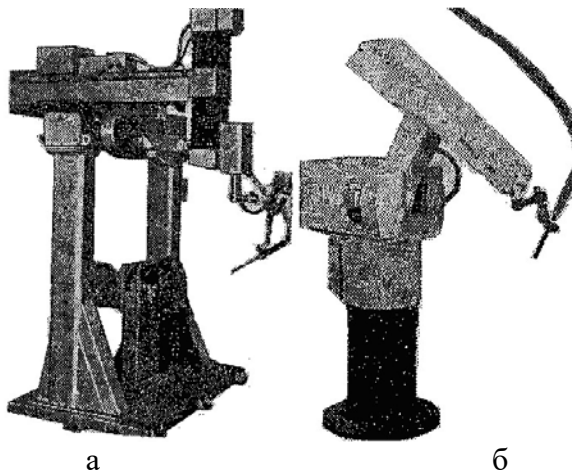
Роботи для зварювання фірми «Шин-Мейва» (Японія): а – PW752; б – RJ65
